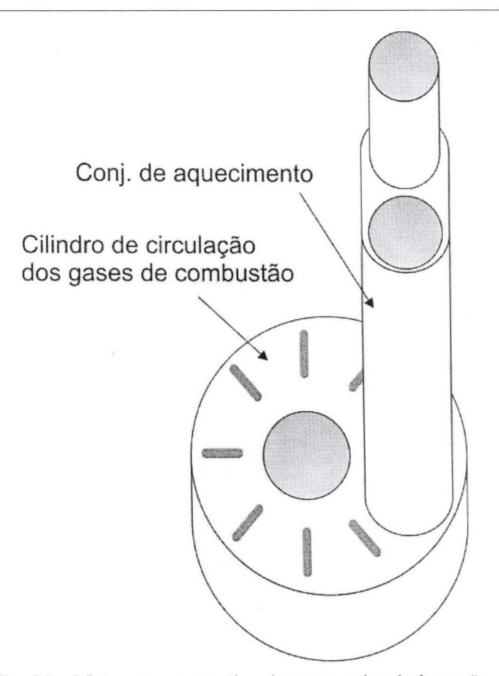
Vista em perspectiva do aquecedor de imersão
